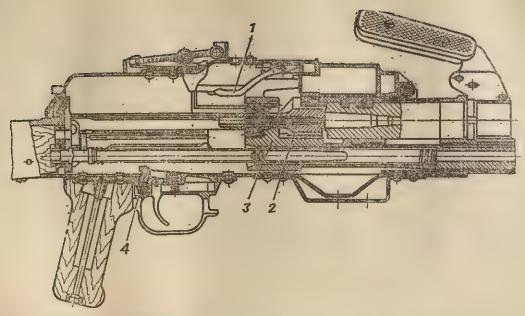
Положение частей и механизмов пулемета до заряжания: 1- рычаг подачи; 2- затвор; 3- затворная рама; 4- спусковой рычаг
